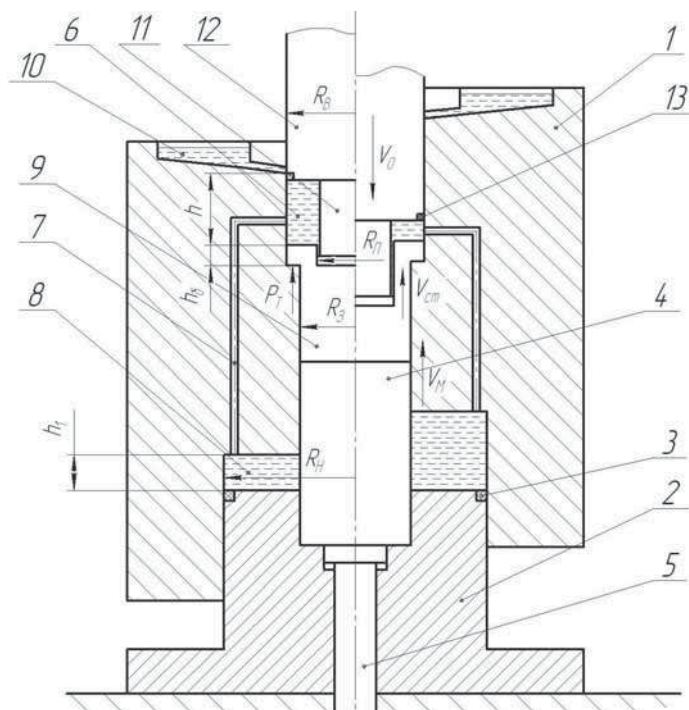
Схема штамп для видавлювання з розтягом сталей порожнистих виробів
